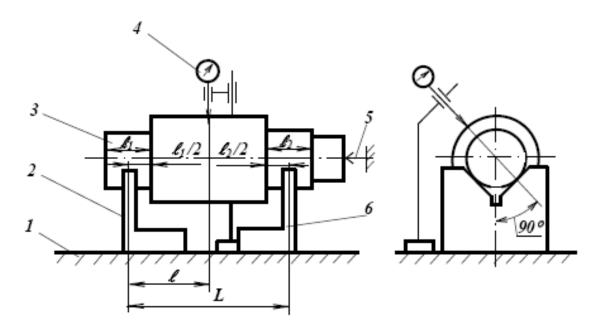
Схема измерения радиального биения наружной поверхности шлиц относительно общей оси шеек под подшипники: 1 — поверочная плита; 2 и 6 — ножевидные призмы; 3 — измеряемая деталь; 4 — индикатор многооборотный; 5 — упор
